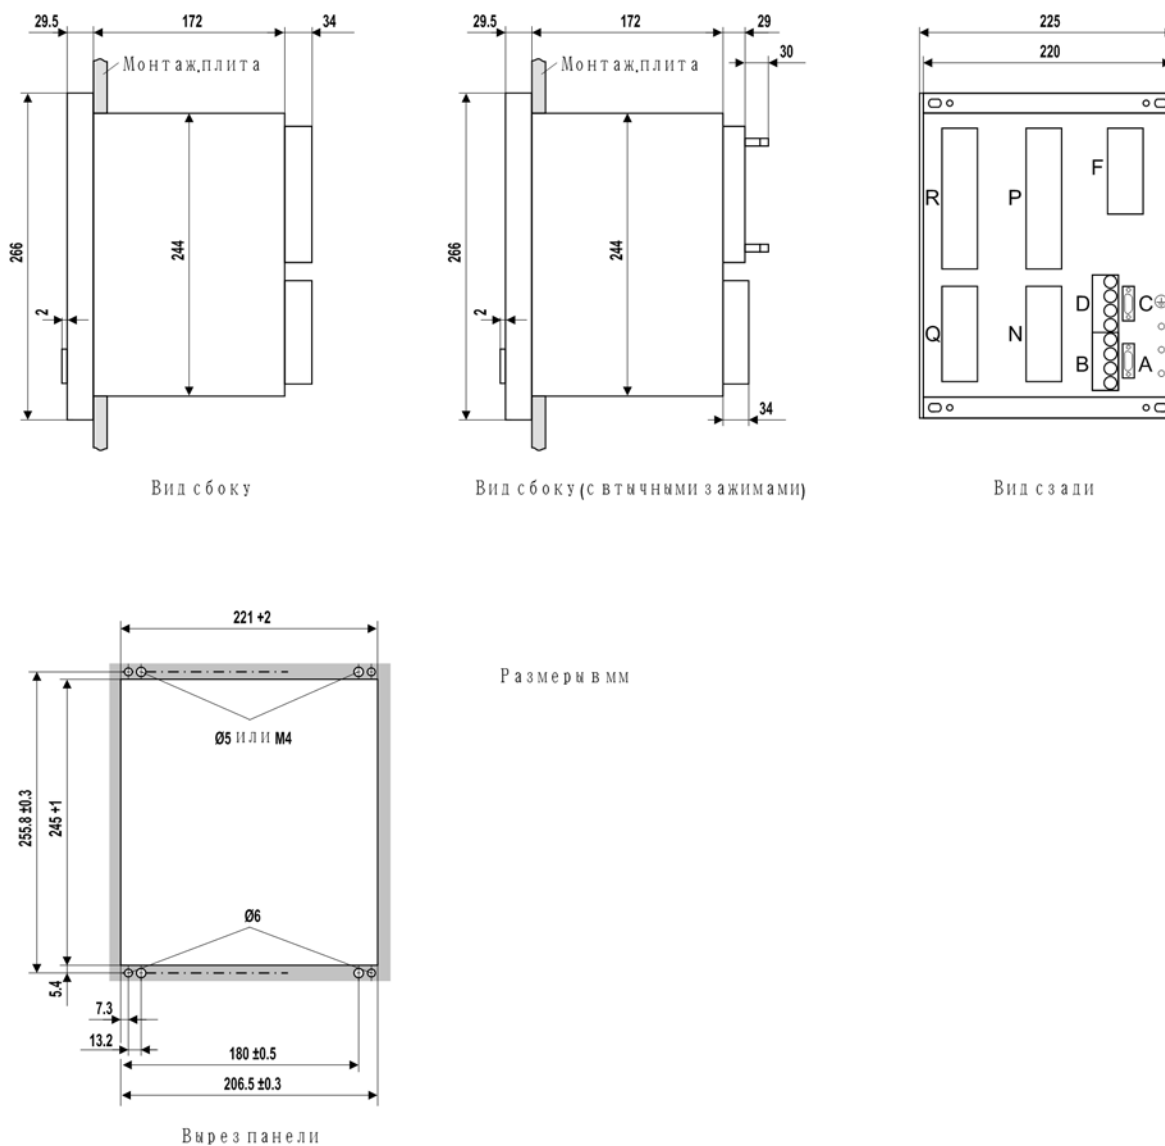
Размеры терминала 7UT613 в корпусе для утопленного монтажа на панели или в шкафу (размер корпуса 1/2)
